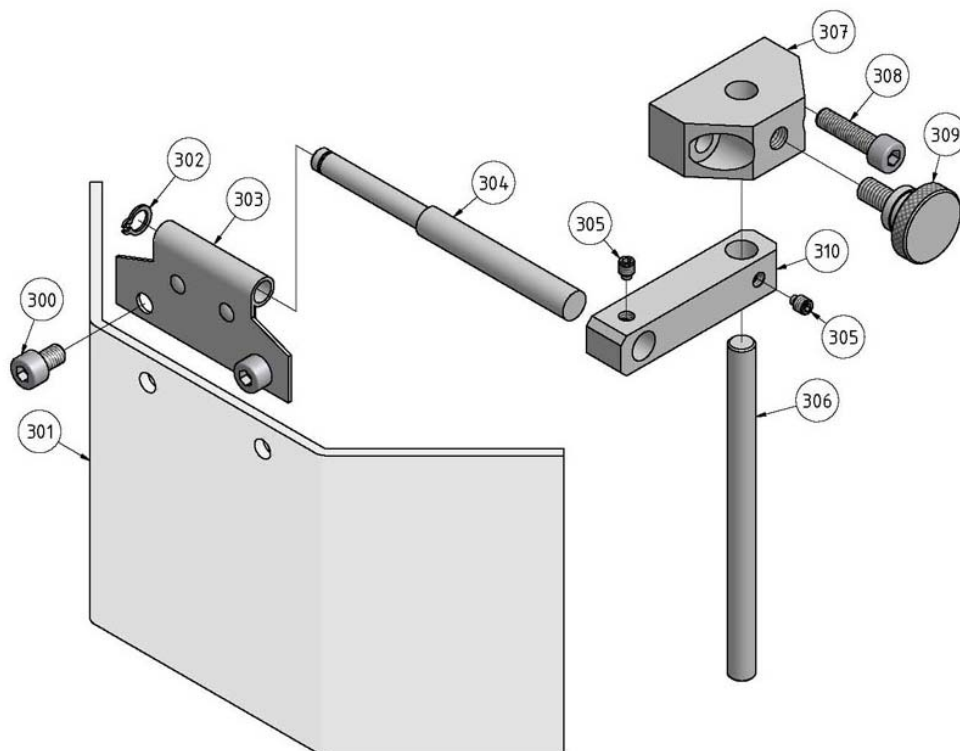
Fräsfutterschutz - Milling chuck protection
